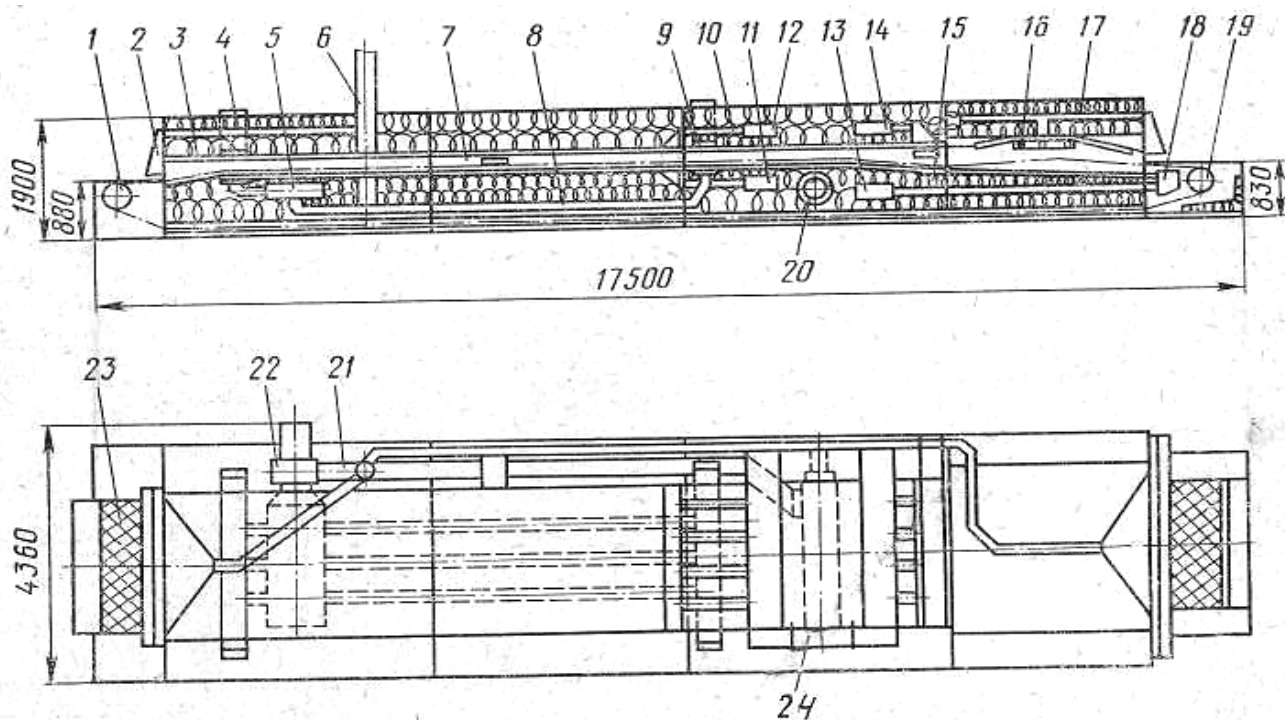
Піч ПХК-25: 1-приводний пристрій; 2-пекарна камера; 3,4-канали; 5-зона зволоження; 6-парові труби; 7-вентиляційна система; 8-натяжний пристрій; 9,14-шибера; 10-топка; 11-камера змішування; 12,13,16-короба; 15-вентилятор; 17-ізоляція; 18-смотрове віконце; 19-запобіжні клапани.
